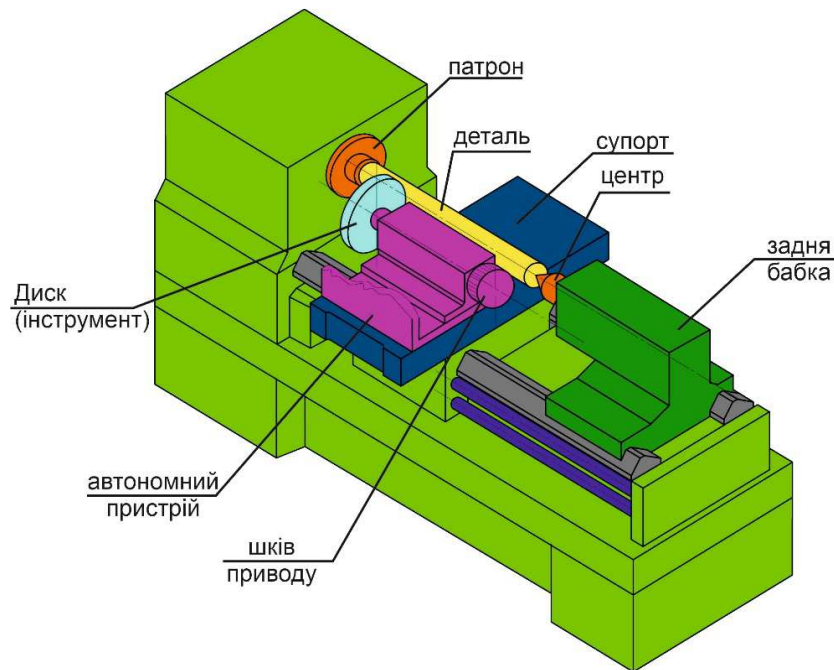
Схема модернізованого токарно-гвинторізного верстата зі спеціальним пристроєм для автономного привода інструменту
